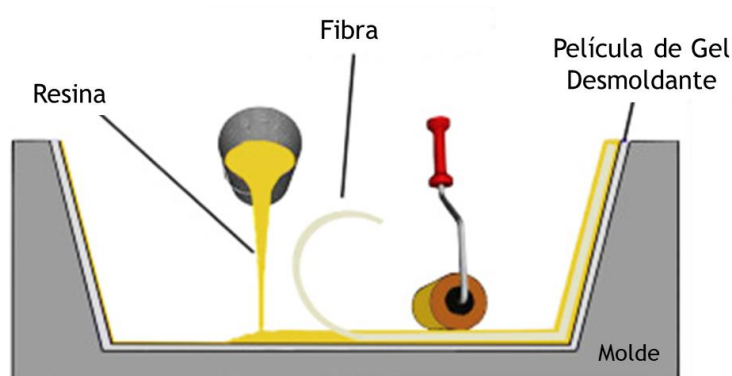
Representação esquemática do processo de moldação manual. Adaptado de [28].
